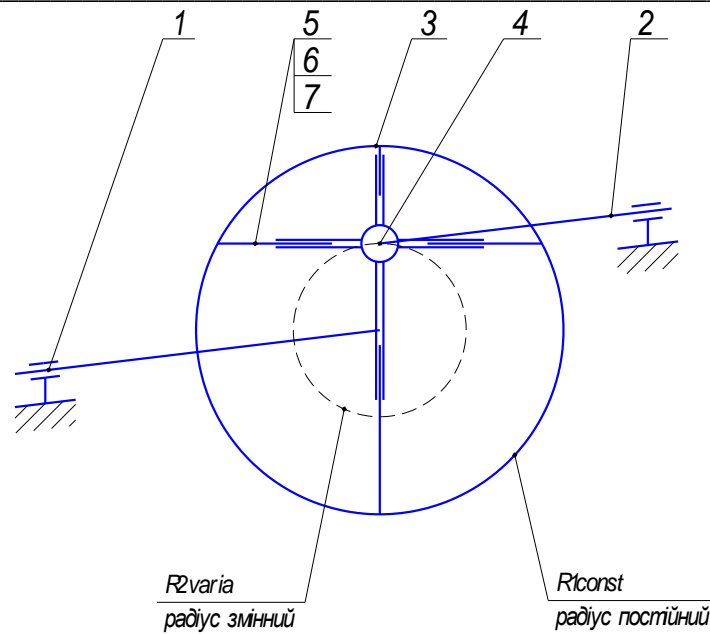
Кінематична схема нового фрикційного варіатора: 1. ведучий вал; 2. ведений вал; 3. диск; 4. ступиця; 5. напрямна; 6. повзун; 7. кулька
